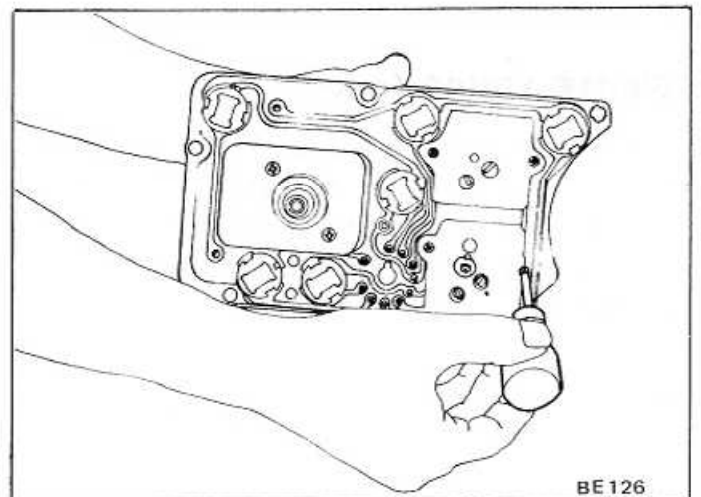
Dépose de l'indicateur de niveau de carburant
